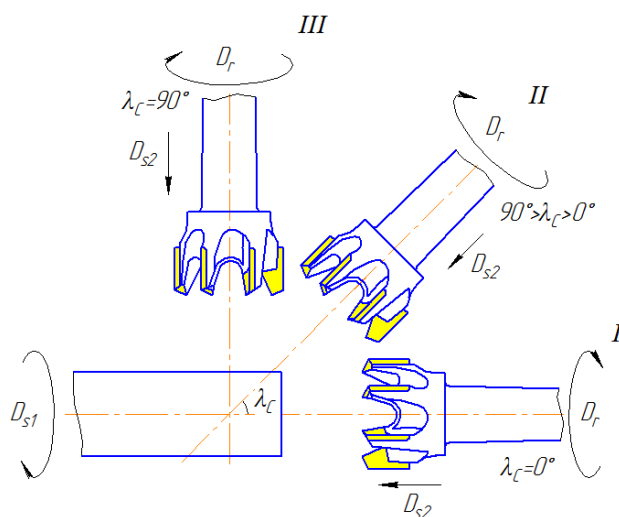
Схемы установки вращающегося инструмента относительно вращающейся детали
